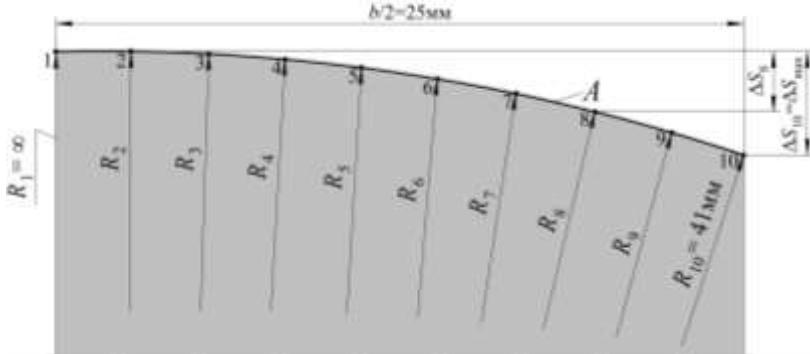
Криволинейная образующая A боковой поверхности наружного зуба
